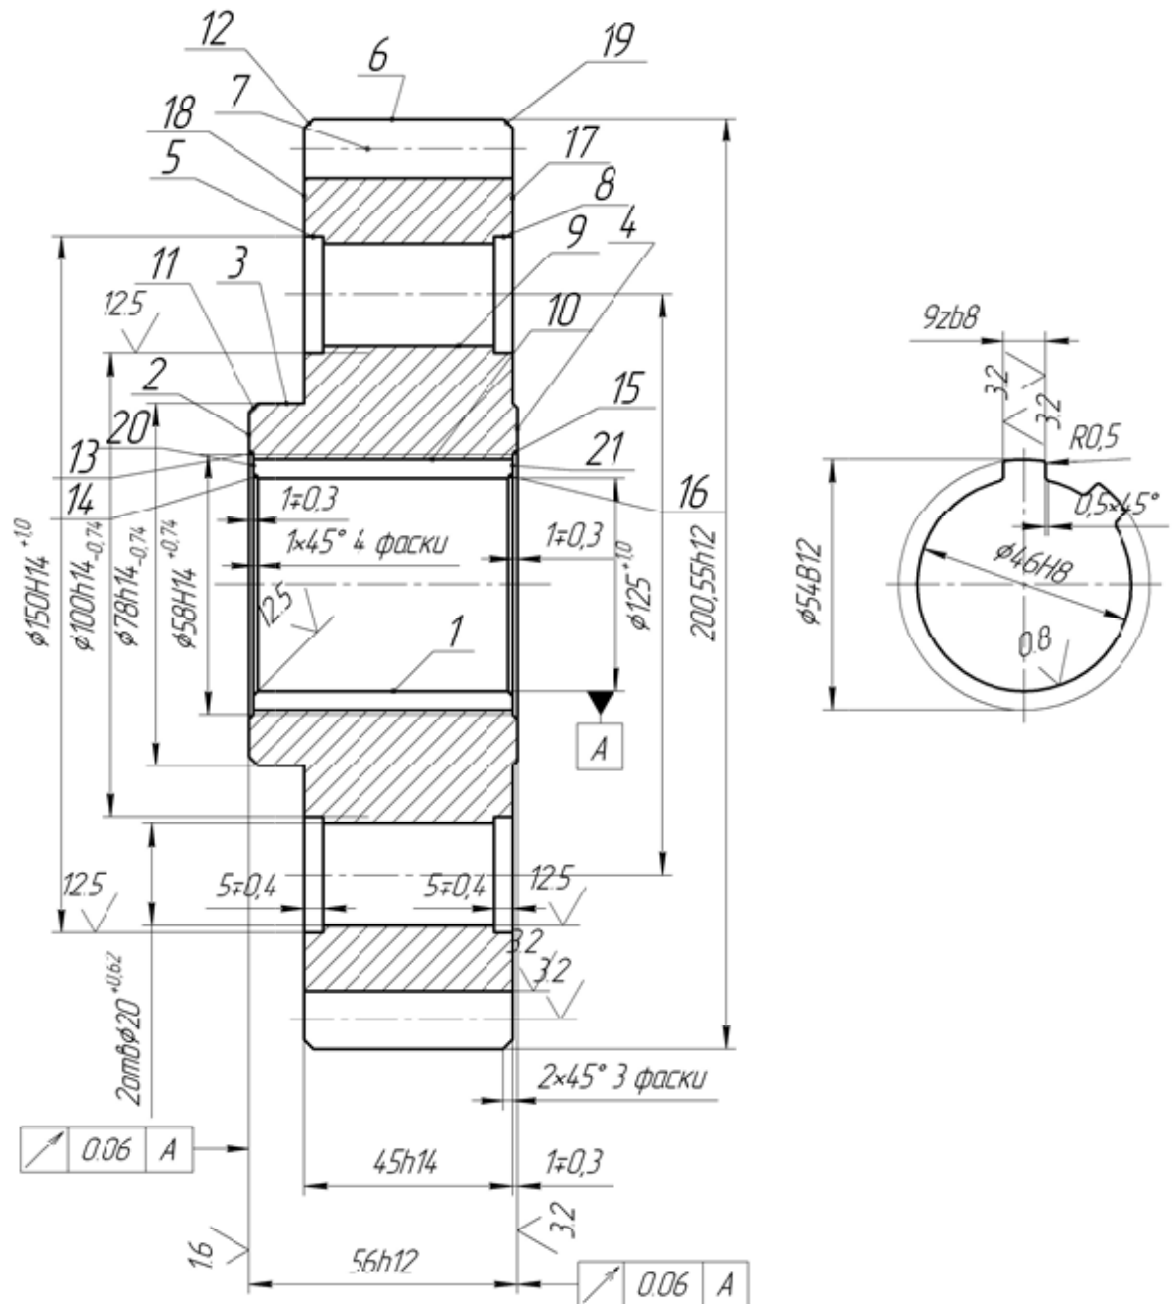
Креслення колеса із зазначенням номерів поверхонь
